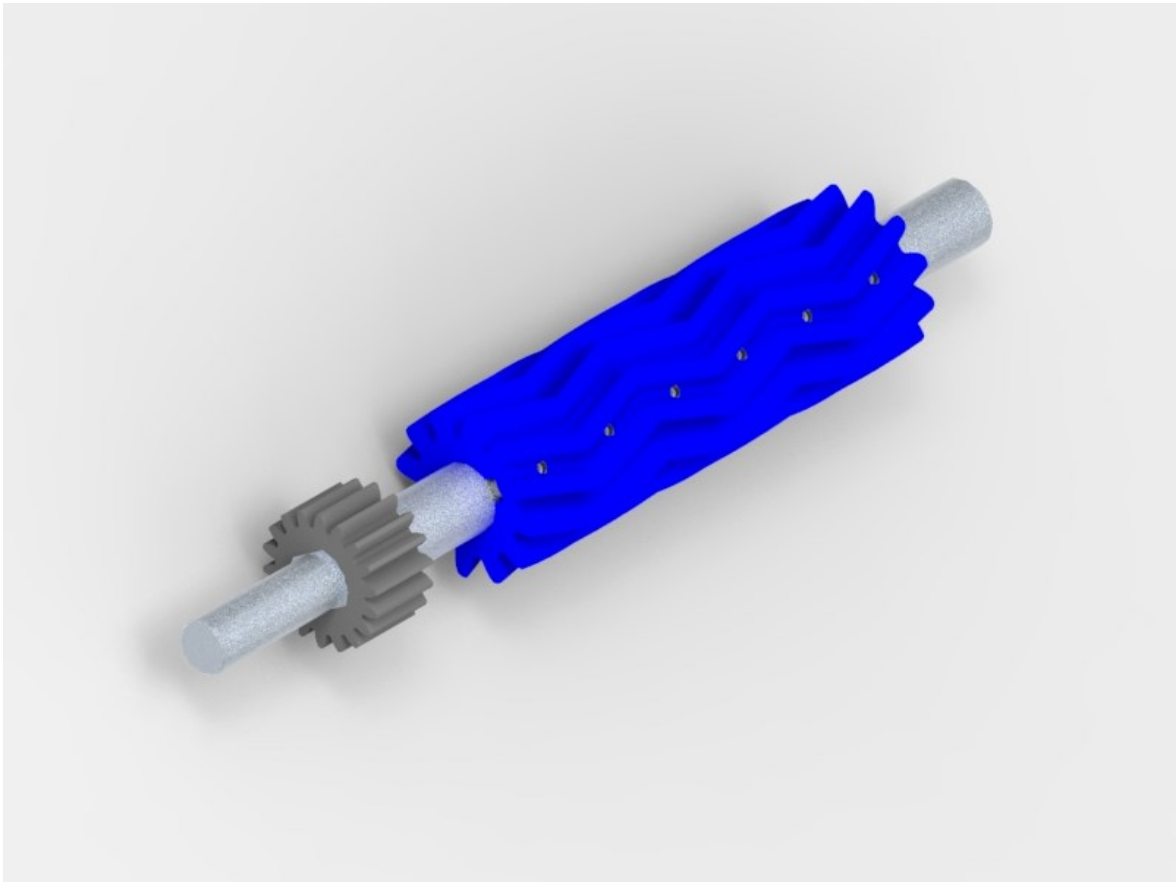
Rendering dell'assieme "asse mobile motore"
